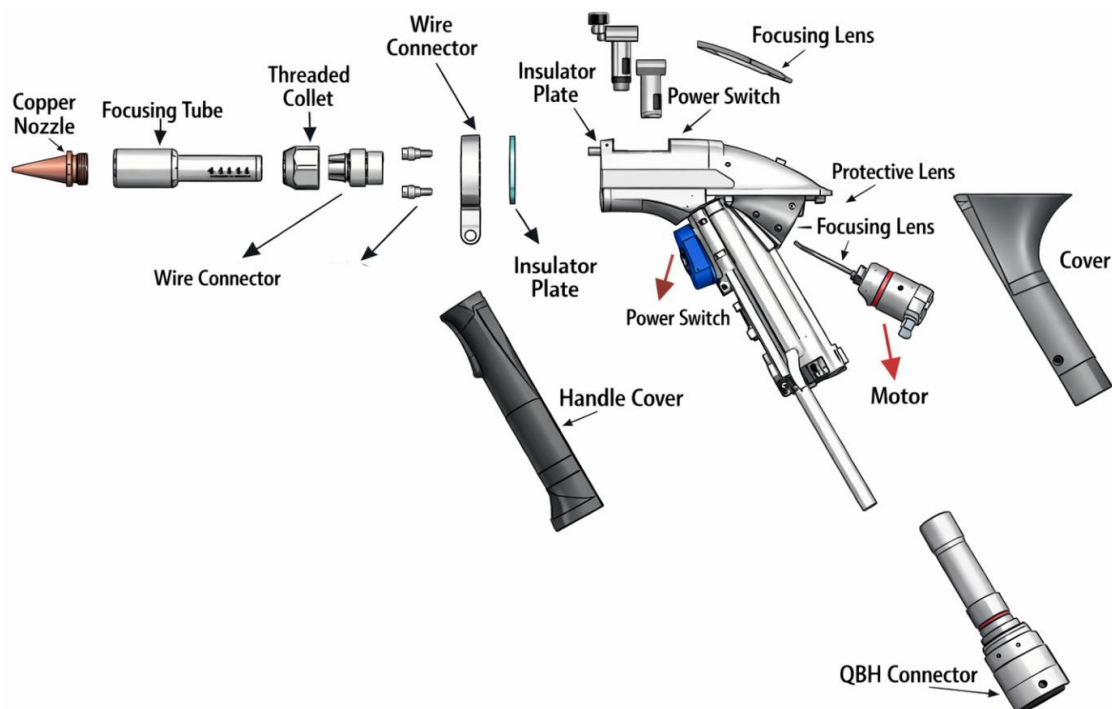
Schéma de la torche de soudage laser portable
